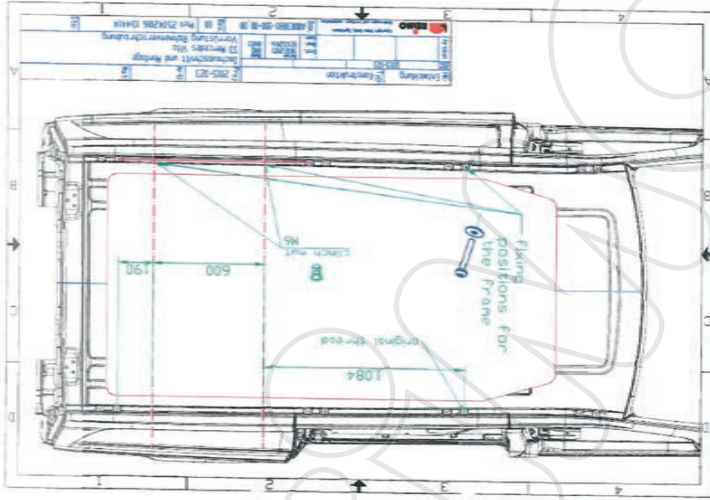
Zeichnung Dachausschnitt 2
